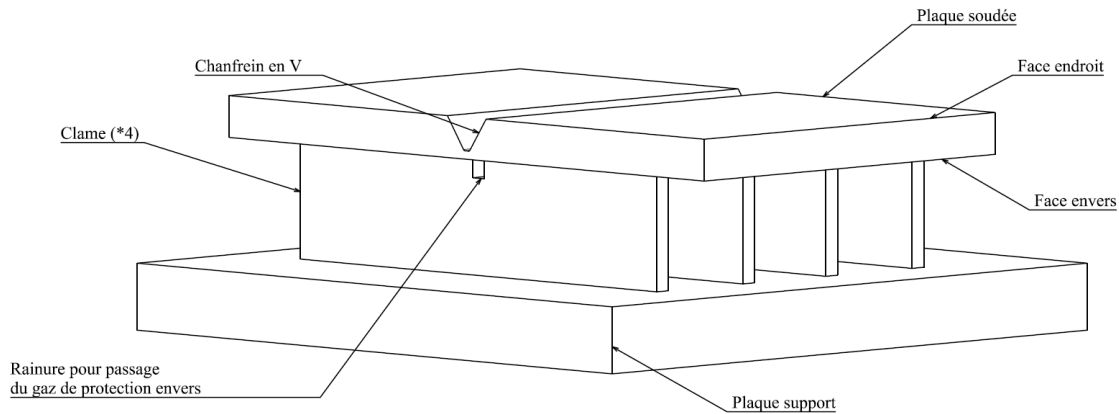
Assemblage de la maquette avec clames et plaque support.
